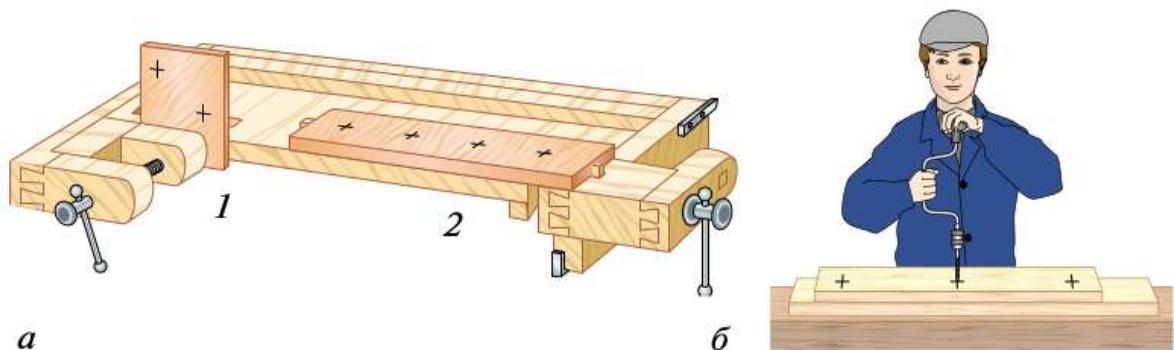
Сверление: а — крепление заготовок при сверлении:
